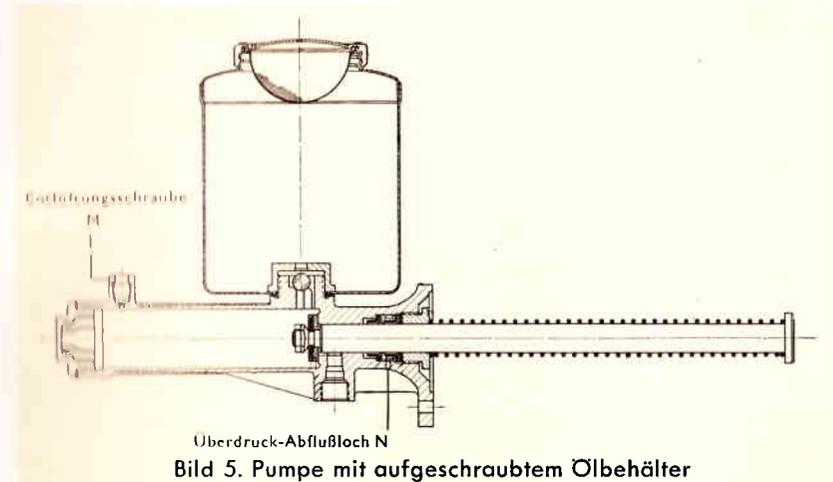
Pumpe mit aufgeschraubtem Ölbehälter
